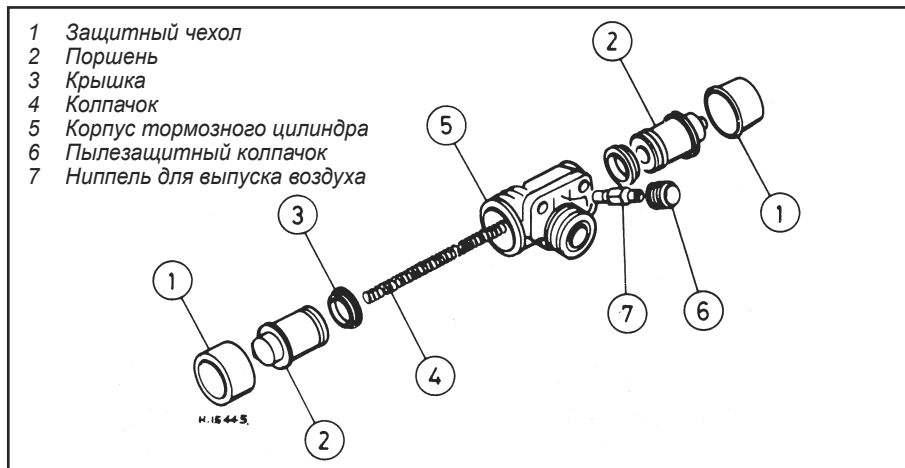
Детали заднего колесного цилиндра (типичные)
